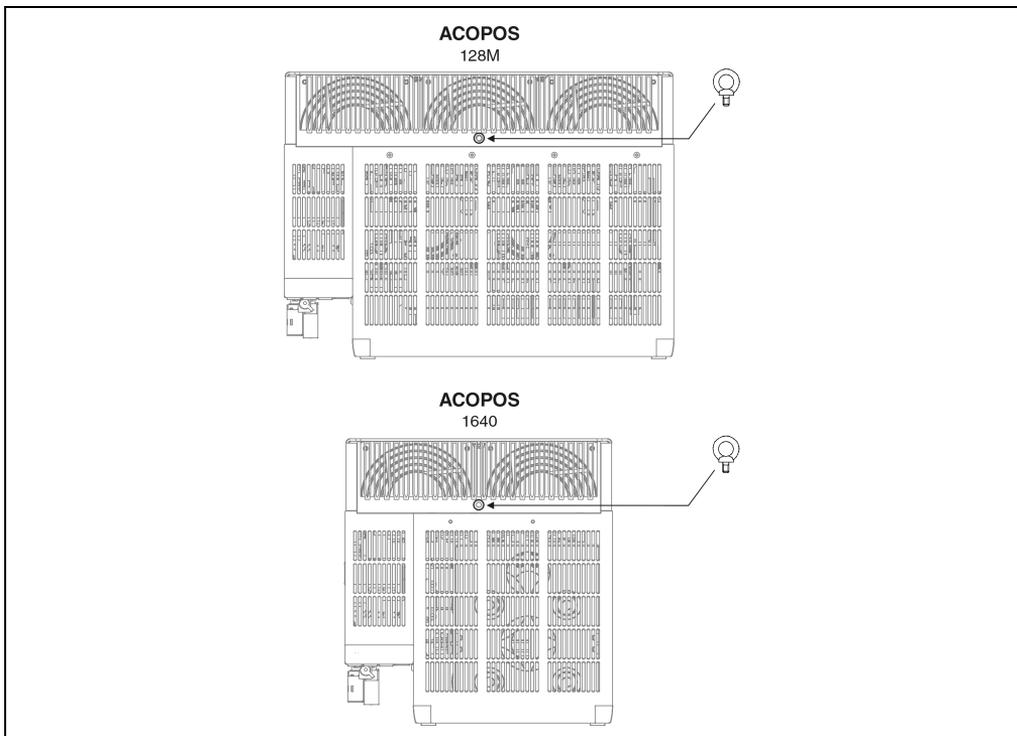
Einschrauben der mitgelieferten Ringschraube bei ACOPOS 1640 und 128M
